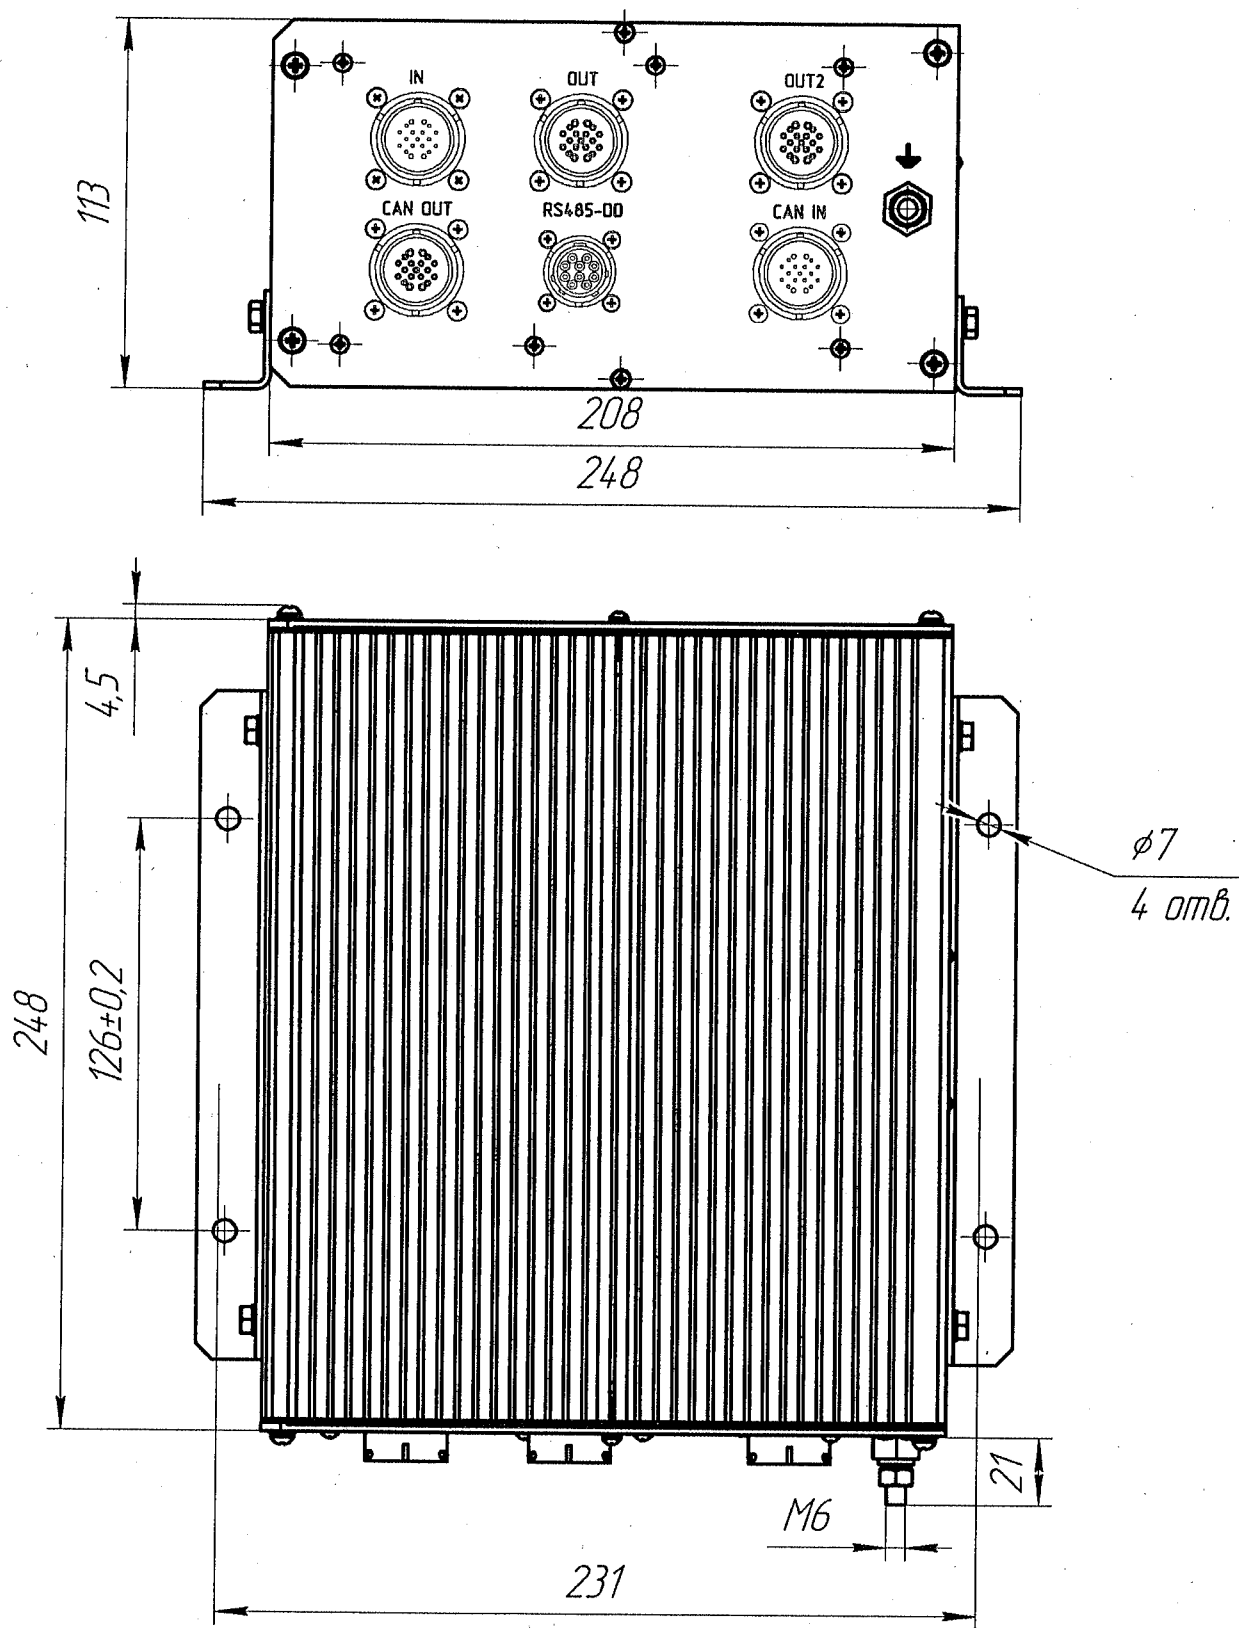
Внешний вид блока ВВД-02 36311-40-00-02
